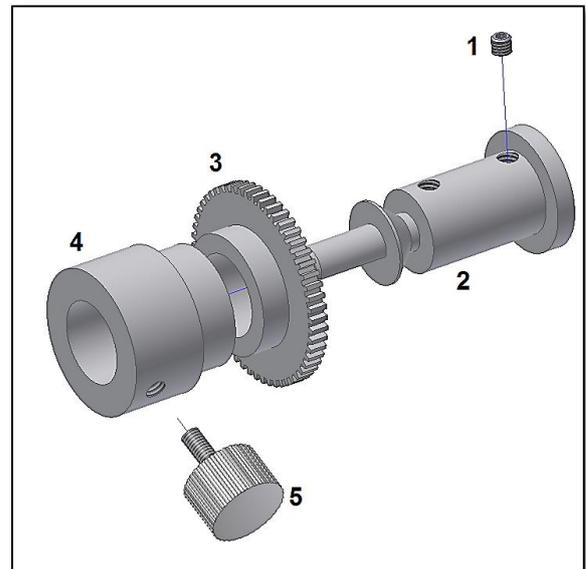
R.A. Zahnräder mit entkoppelbarer Welle.
